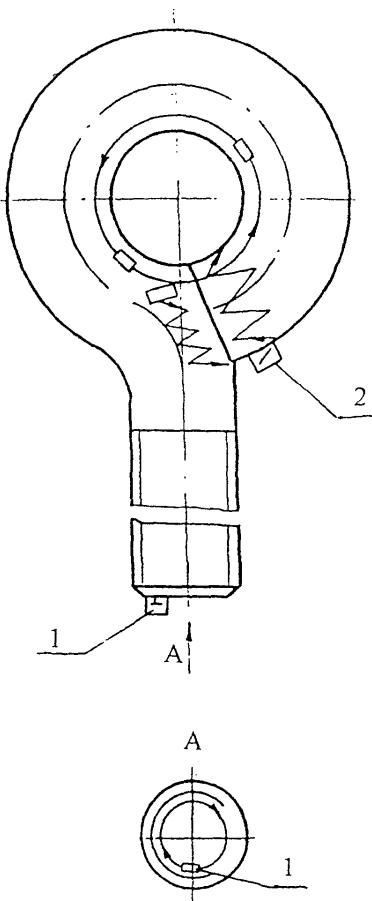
Схема контроля крюка ПБК4 - 06.00.001
